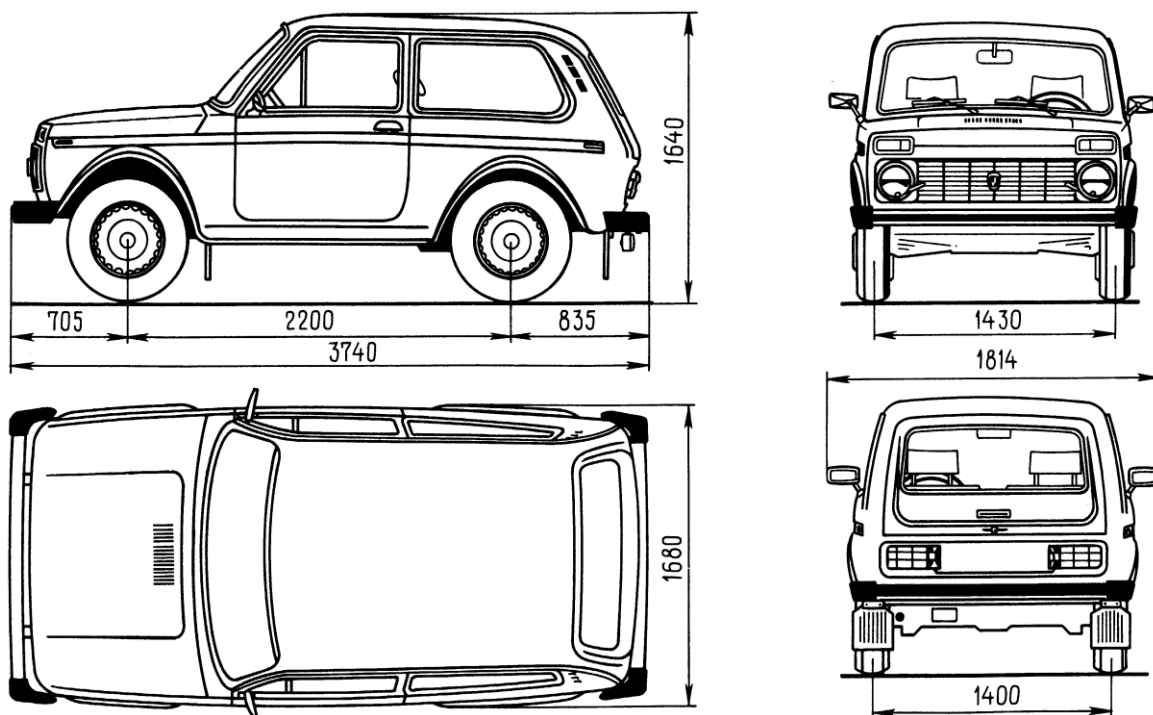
Габаритные размеры автомобиля ВАЗ-2121
